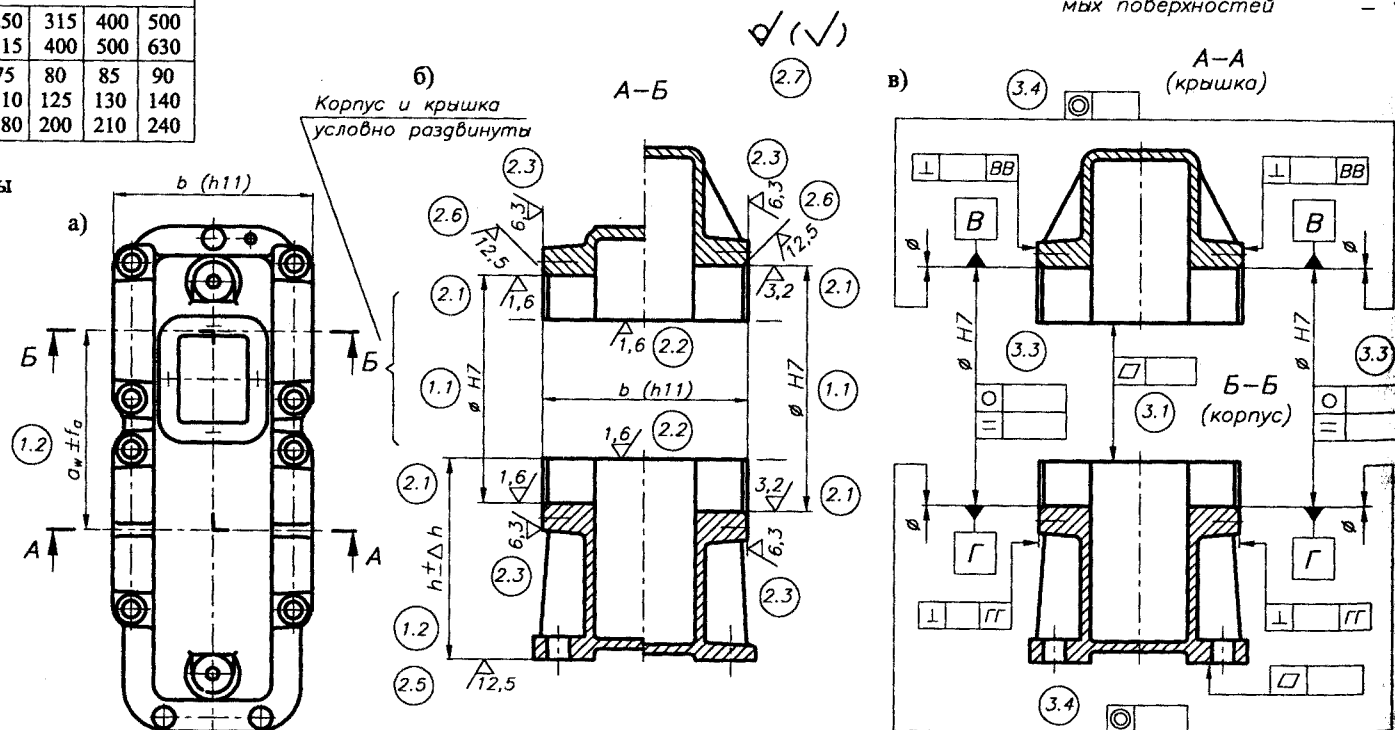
Обозначение на корпусных деталях редукторов:
